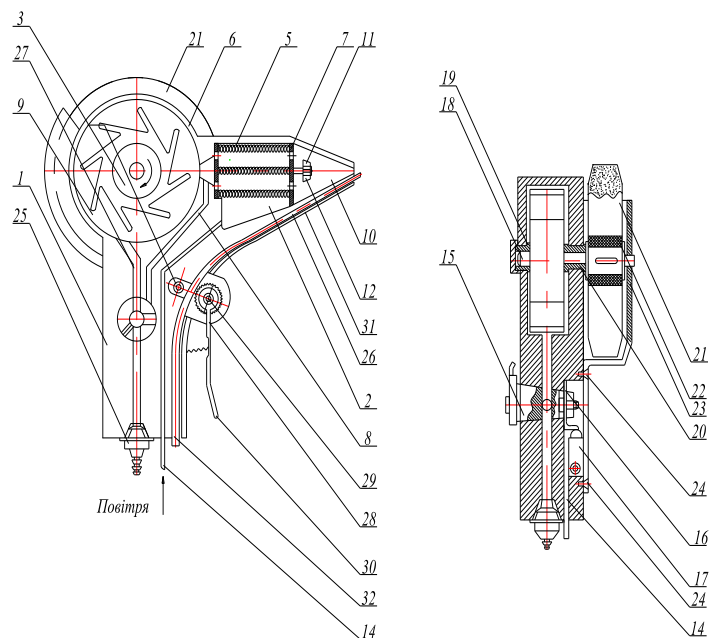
Пристрій для зварювання полімерних матеріалів
